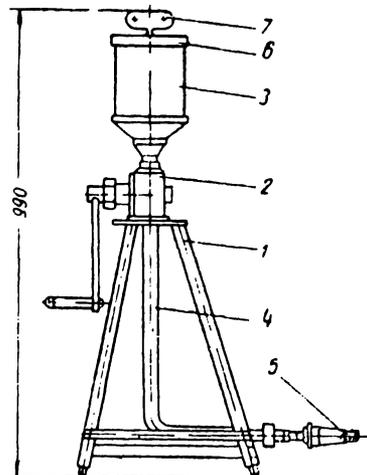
Насос шестеренчатый для смазки колес вагонеток
